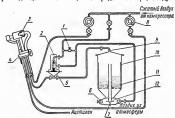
Схема аппарата для газопламенного наплавления пластмасс:
